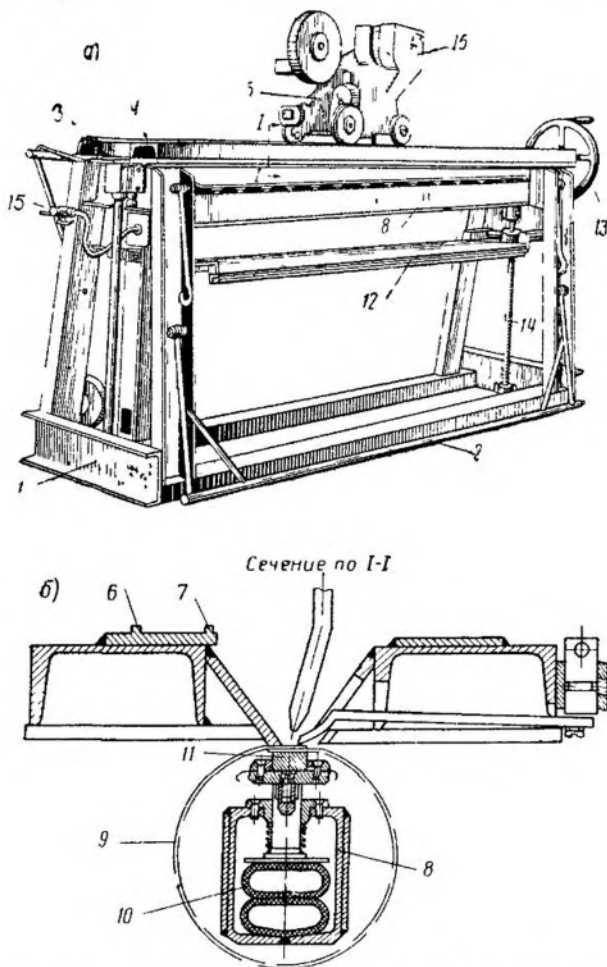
Установка для сварки воздухопроводов трактором ТС17-М модель ГСТМ-11
